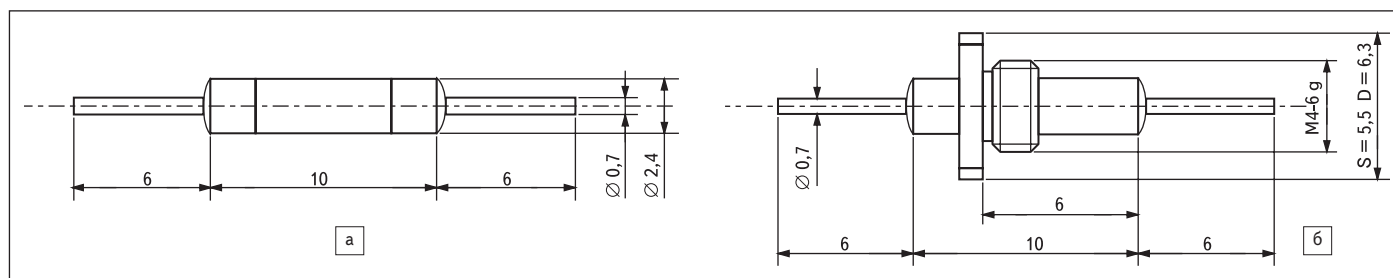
Фильтры Б24: а) для пайки в устройство по корпусу фильтра; б) для пайки с помощью резьбовой втулки
